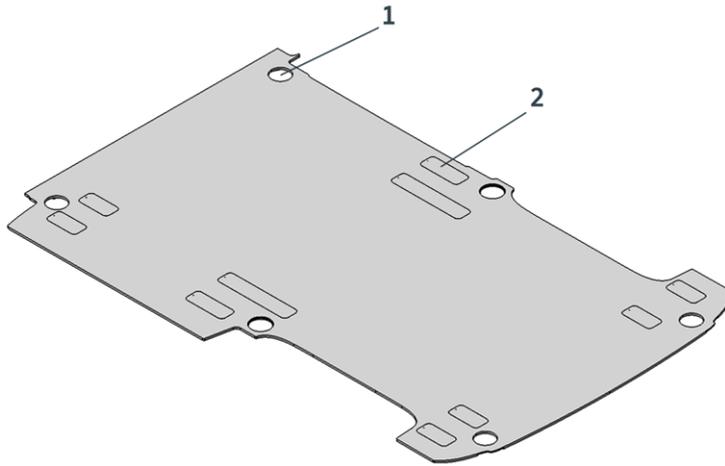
Piso universal (5BM); aquí en la figura: Transporter con batalla corta y puerta corredera a la derecha
